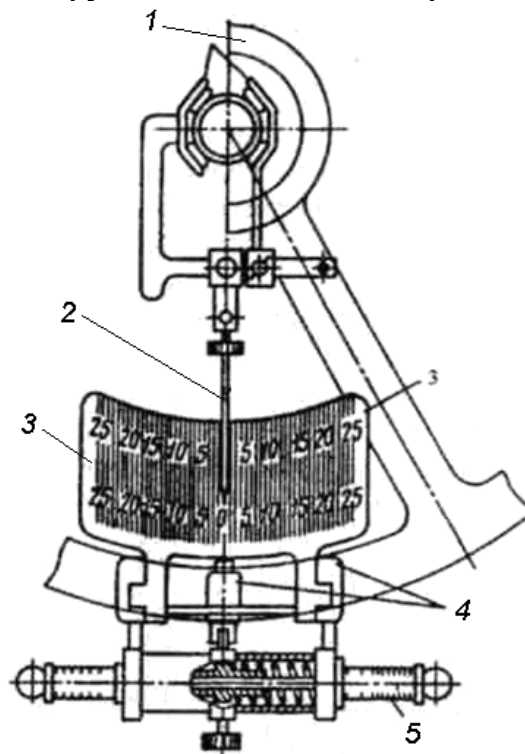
Прилад К-402 для перевірки рульового керування:
